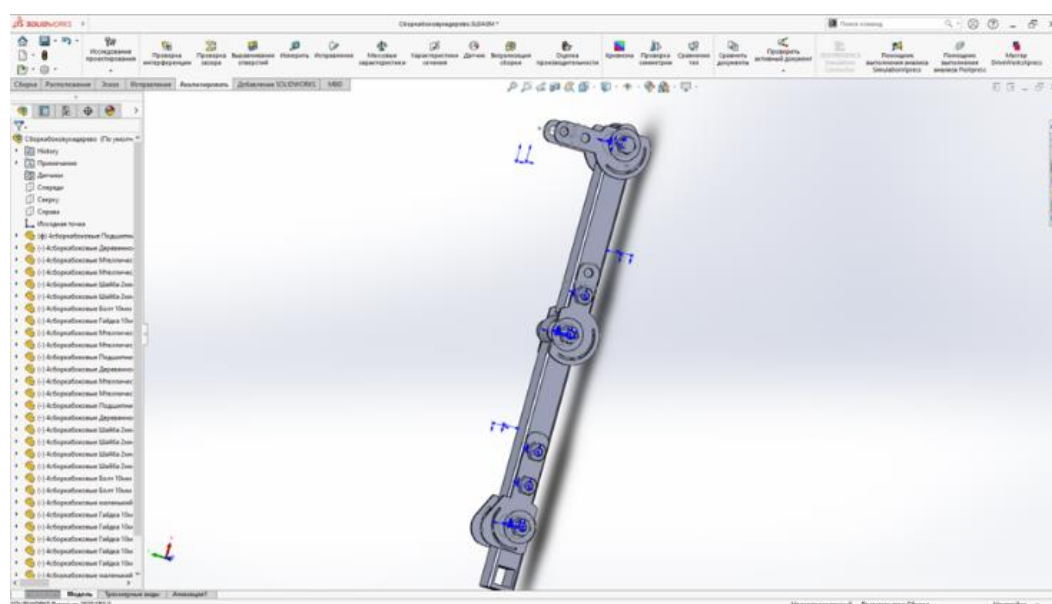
Боковой механизм для реабилитации нижних конечностей
